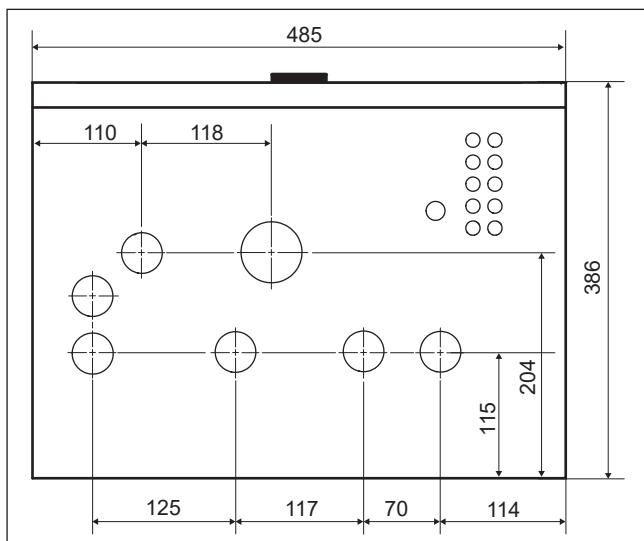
Rozměry vnitřní závěsné jednotky AWB 9/17
